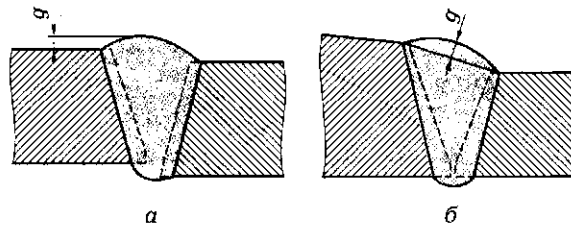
Измерение выпуклости g стыкового шва при разном уровне лицевых поверхностей деталей, вызванном их смещением при сборке соединения под сварку (а) и неодинаковой толщиной деталей (б)
